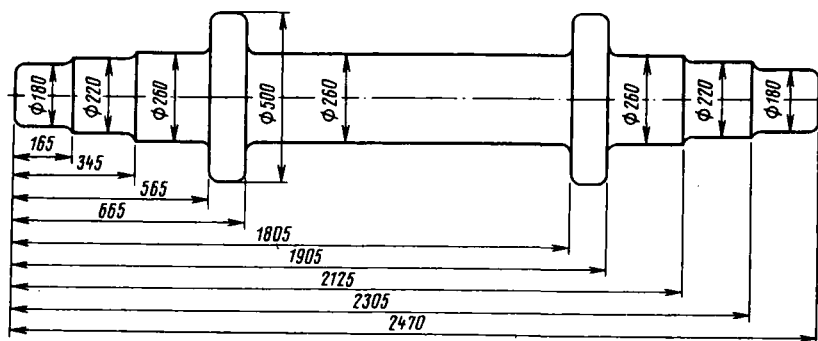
Главный приводной вал эскалатора Н-40 очереди II
